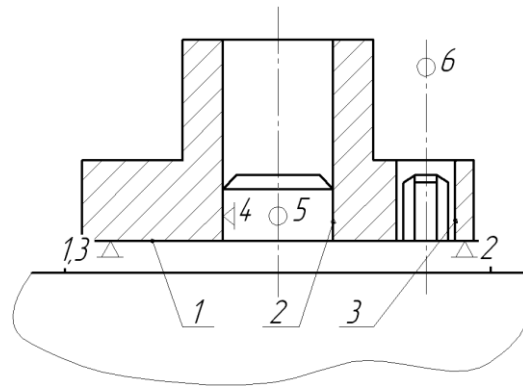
Базування заготовки корпуса фланцевого типу на площину, коротку виточку і отвір
